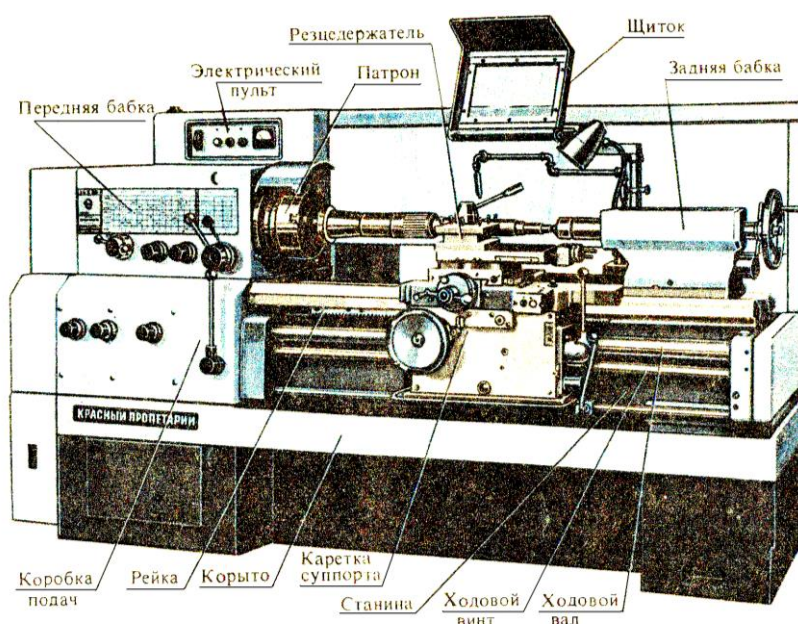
Общий вид токарно-винторезного станка мод. 16К20
